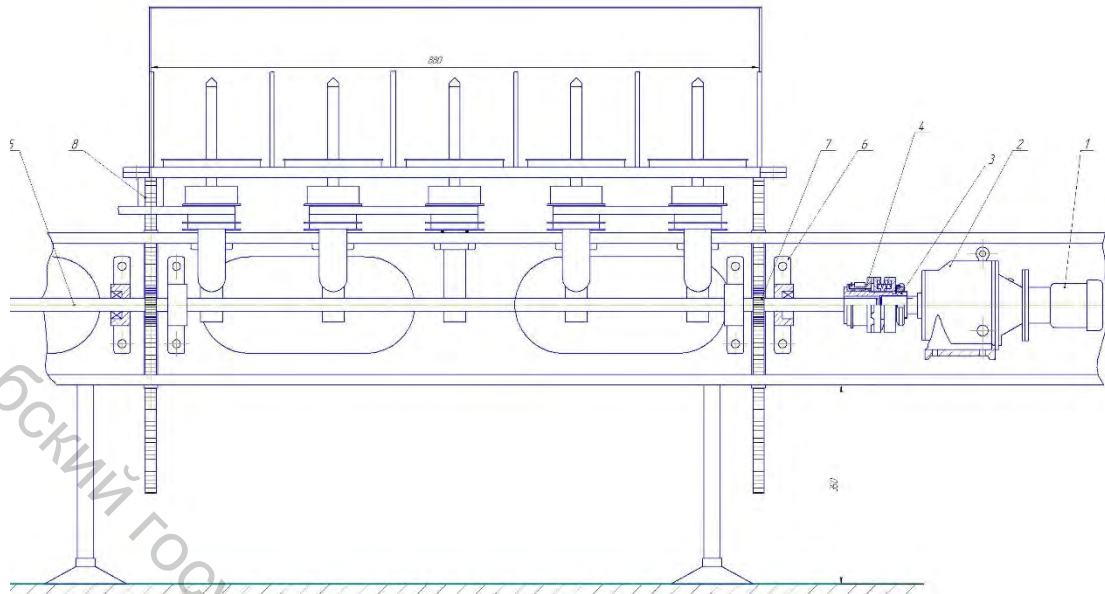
Сборочный чертеж мотального механизма модернизированной крутильной машины
